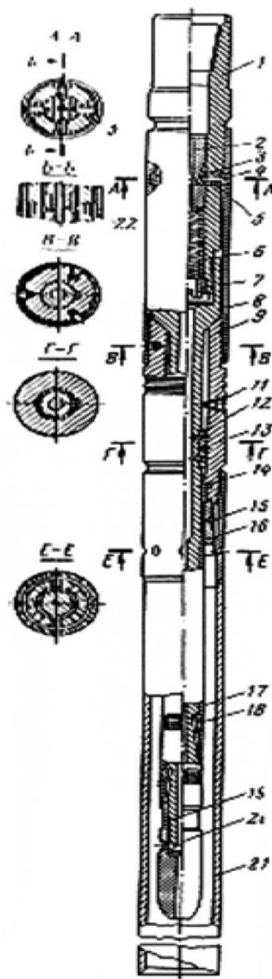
Гидравлический спусковой механизм, совмещенный с верхней частью корпуса
